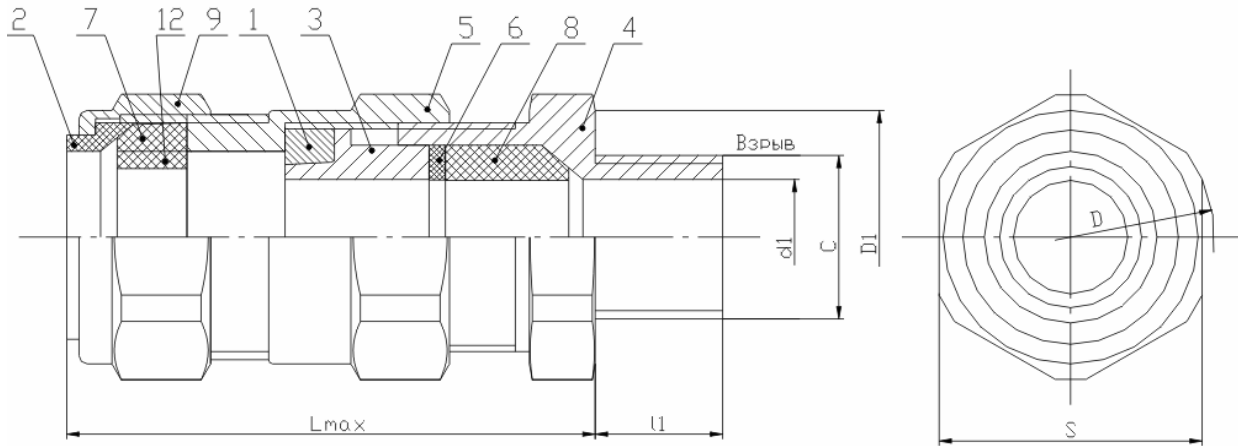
Конструкция кабельного ввода для монтажа бронированного кабеля
